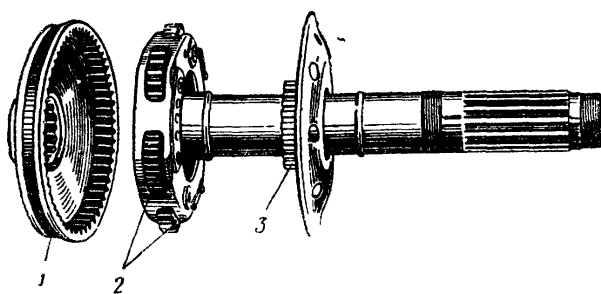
Редукторы рядных двигателей с цилиндрическими шестернями
